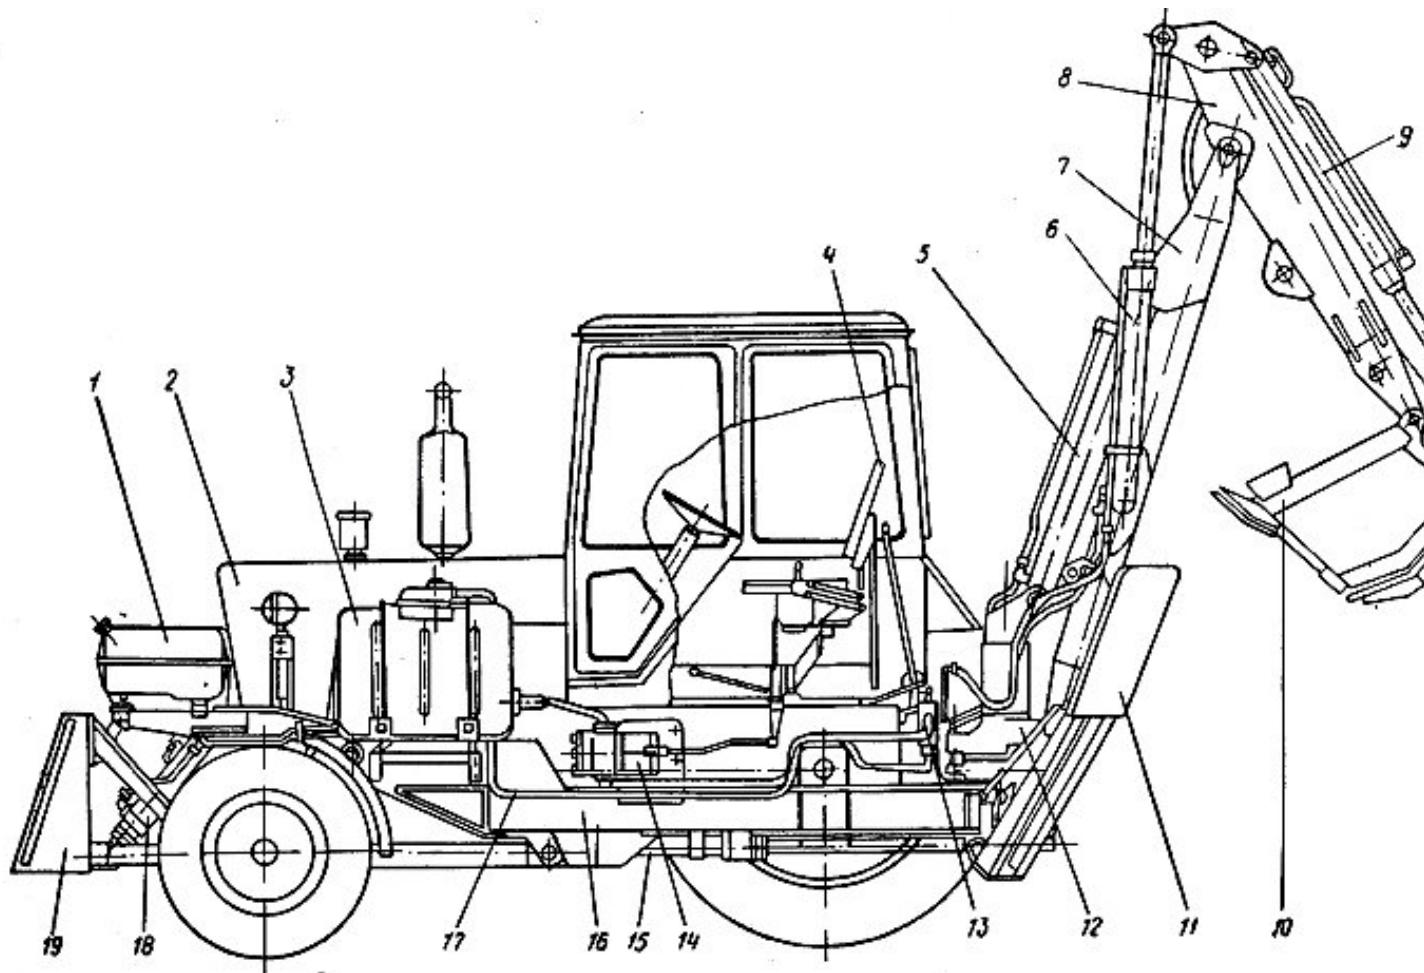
Общий вид экскаватора ЭО-2621В:
